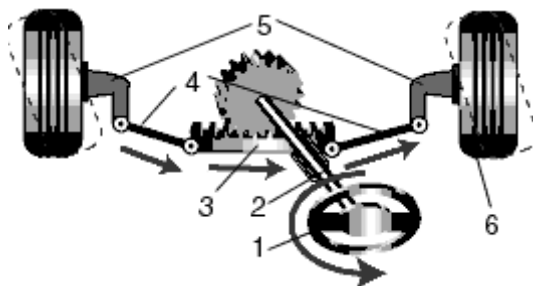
Схема рулевого управления с механизмом типа «шестерня-рейка» 1 - рулевое колесо; 2 - вал с приводной шестерней; 3 -
